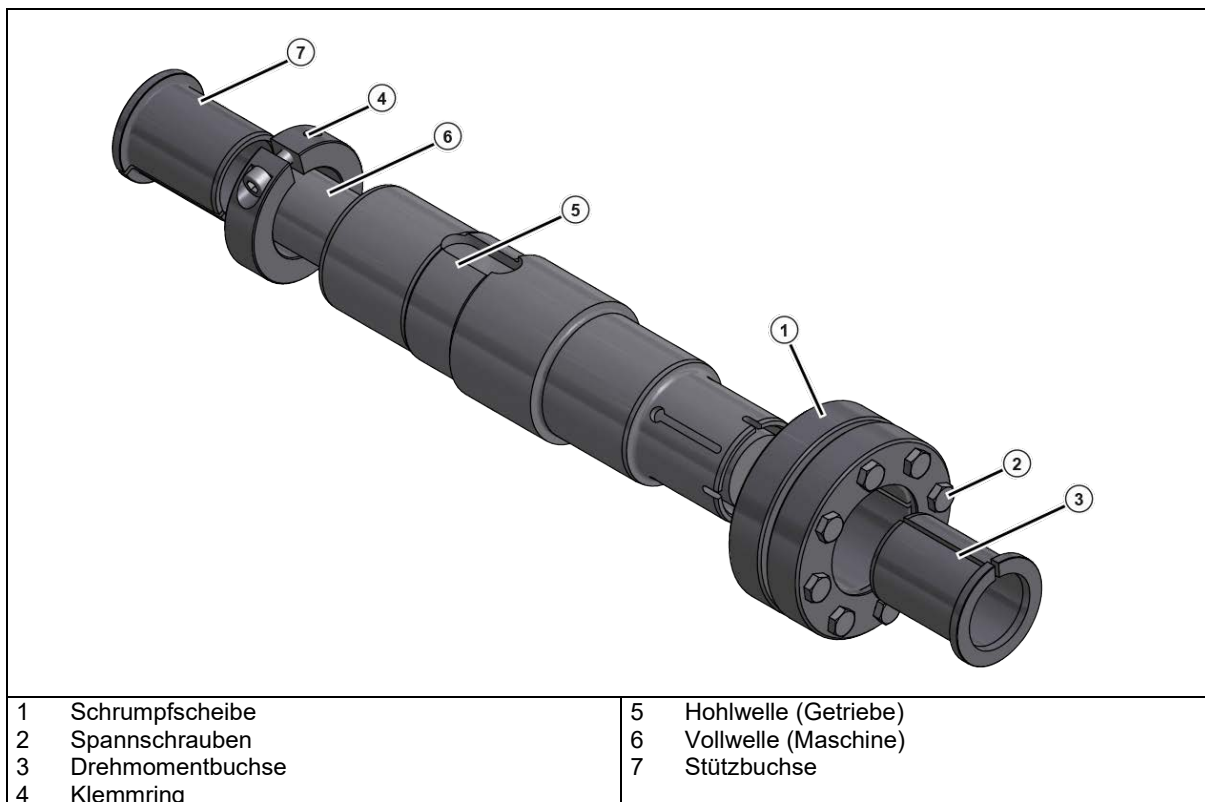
GRIPMAXX™, Explosionsdarstellung
